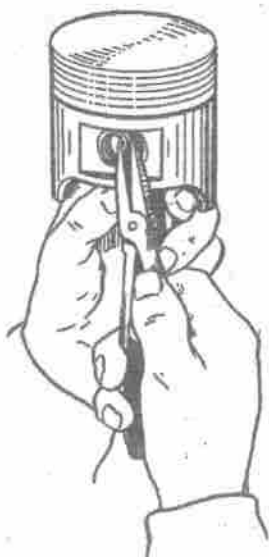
Entfernen der Sicherungsringe des Kolbenbolzens
